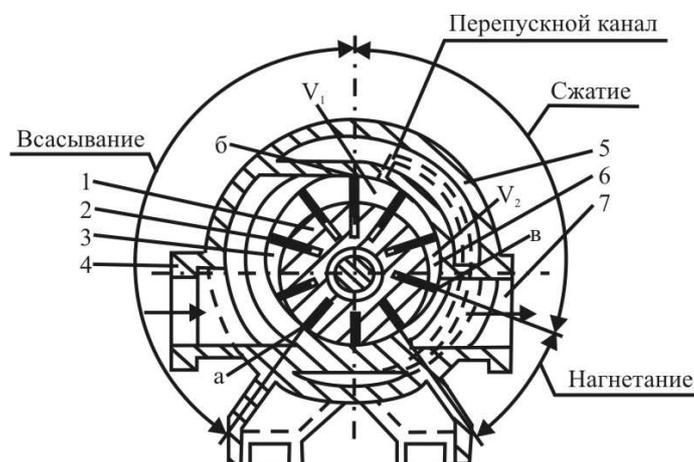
Ротационный компрессор с катящимся ротором:
